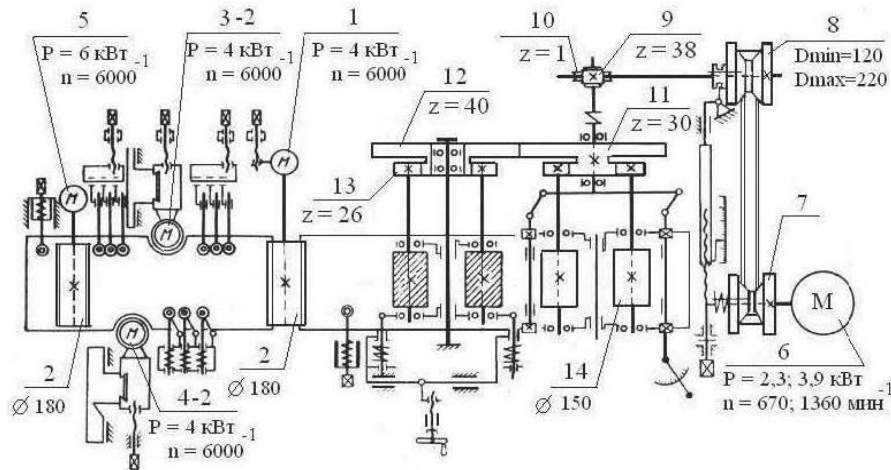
Кинематическая схема четырехстороннего продольно-фрезерного станка С16-4А
